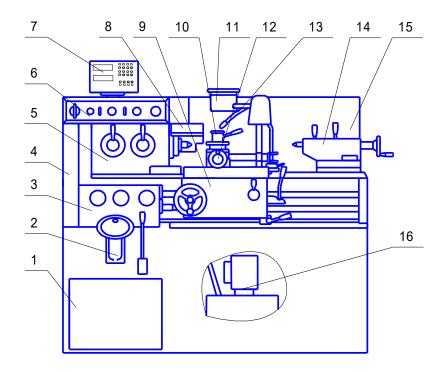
а Расположение составных частей станка исп. Редуктор Перечень составных частей станка исп. Редуктор приведен в таблице 4а
